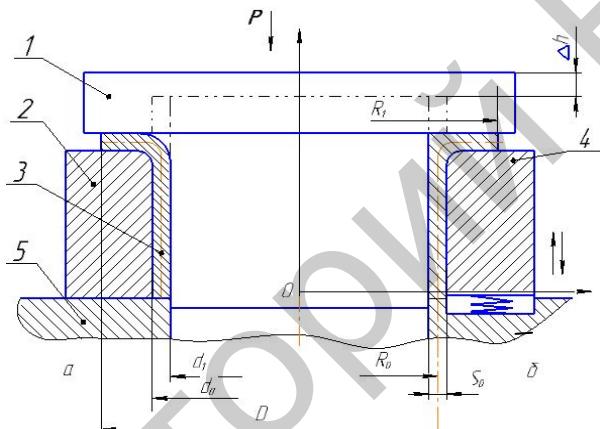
Схема раздачи и осадки трубной заготовки:
